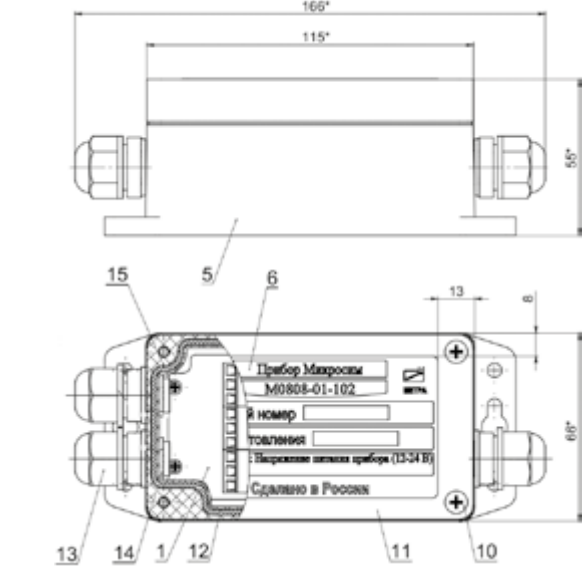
Внешний вид, габаритные и присоединительные размеры Микросим M0808-01-102.
